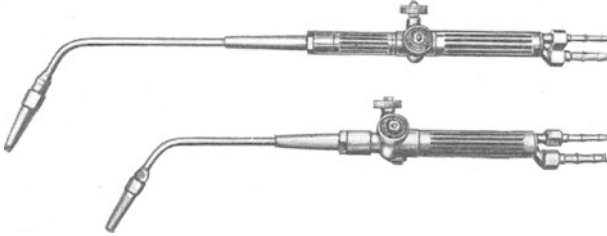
Einzel- (unten) und Wechselschweißbrenner für Azetylen.
